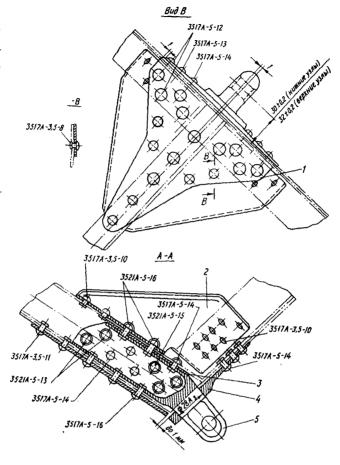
Установка узла крепления моторамы на шп. № 1 на самолетах с сер. № 1Г112-01: 1— накладка Ш0106-11-1/2; 2— уголок Ш0106-14-1/2 (для верхних узлов) или Ш0107-14-1/2 (для нижних узлов); 3— прокладка Д16АТл.0,3-2,0 мм (по необходимости); 4— кница Ш0106-2-1/2 (верхняя) или Ш0107-2-1/2 (нижняя); 5— ухо Ш0106-13-1 (нижнее правое), Ш0106-13-2 (нижнее левое), Ш0106-13-3 (верхнее правое) или Ш0106-13-4 (верхнее левое)
